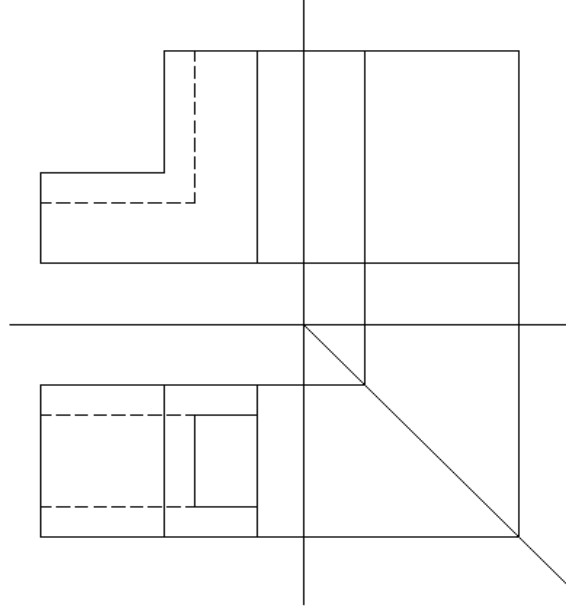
Temel boyutların yatay düzleme taşınması
